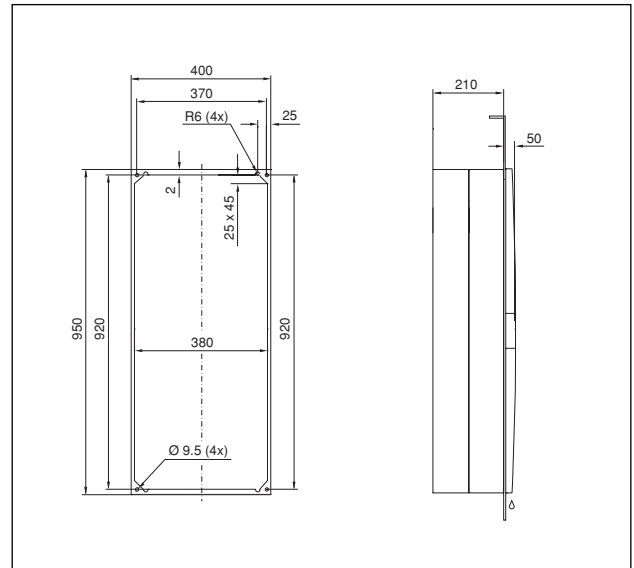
SK 3304.xxx, SK 3305.xxx Komplet inbyggnad
